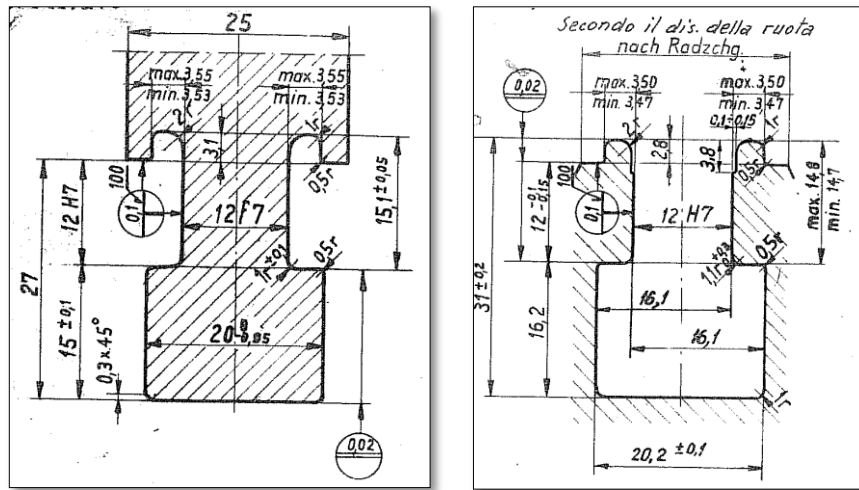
dimensioni del piede palare e della cava sul disco del 6° stadio della turbina n° 2.
